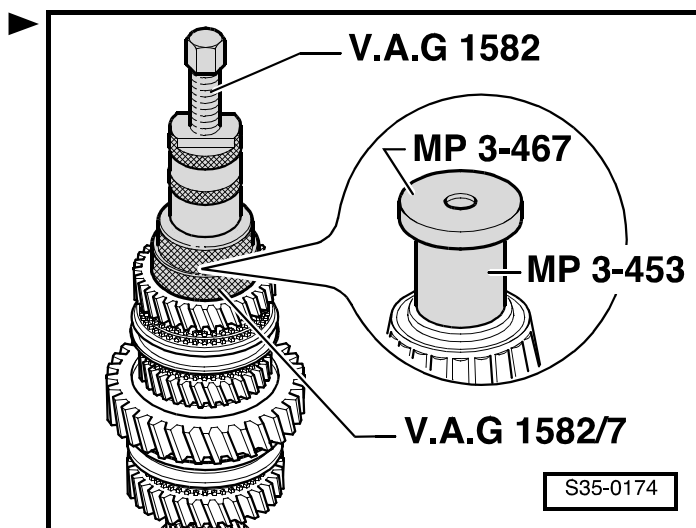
Извлечение скользящей муфты и каретки синхронизатора для 3-ей и 4-ой передач с шестерней 4-ой передачи
